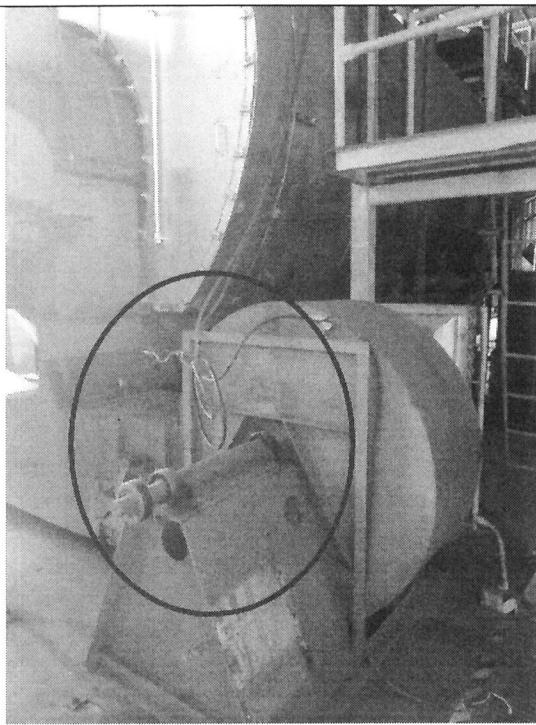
Desmontaje de motor unidad parrilla quemador.
